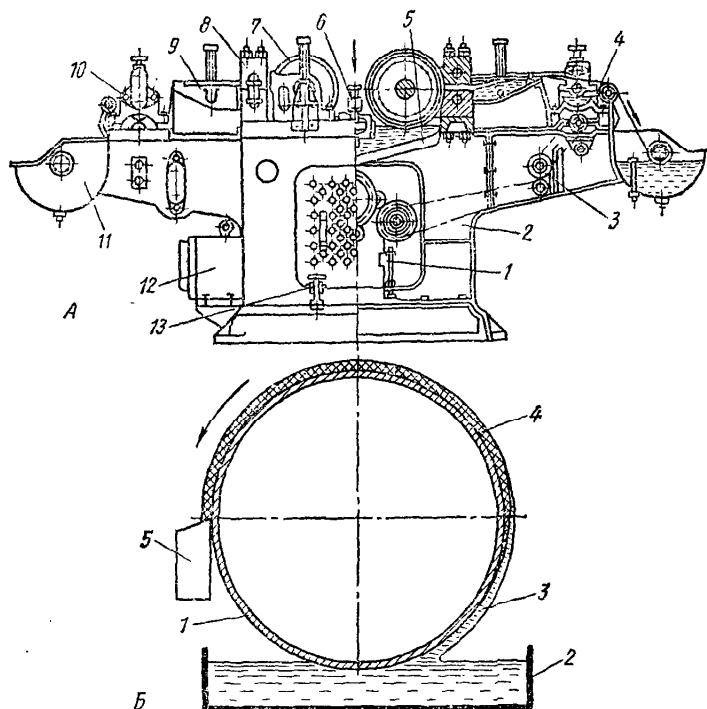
Агрегат для изготовления воскопы АИВ-100:
